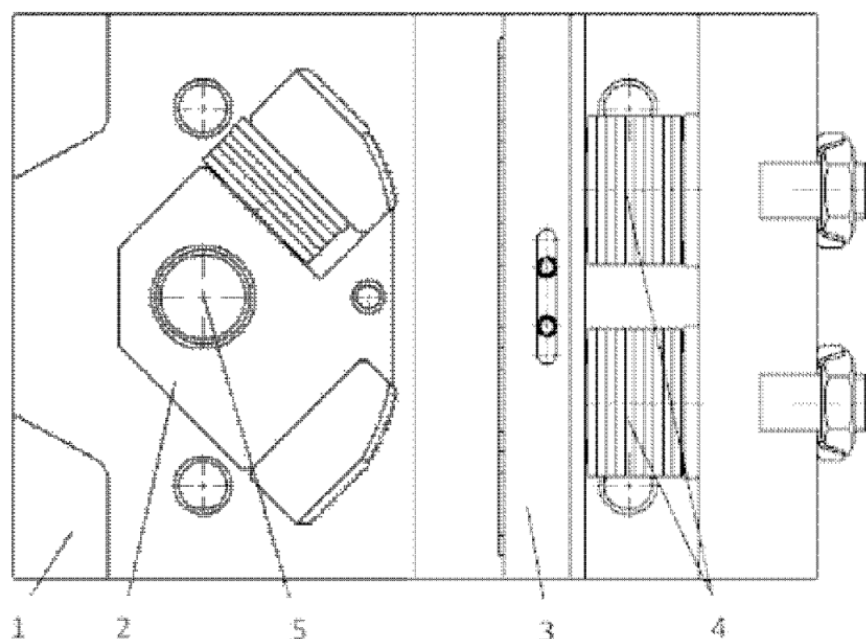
Схема конструкции ловителя по патенту RU 2 718 706
